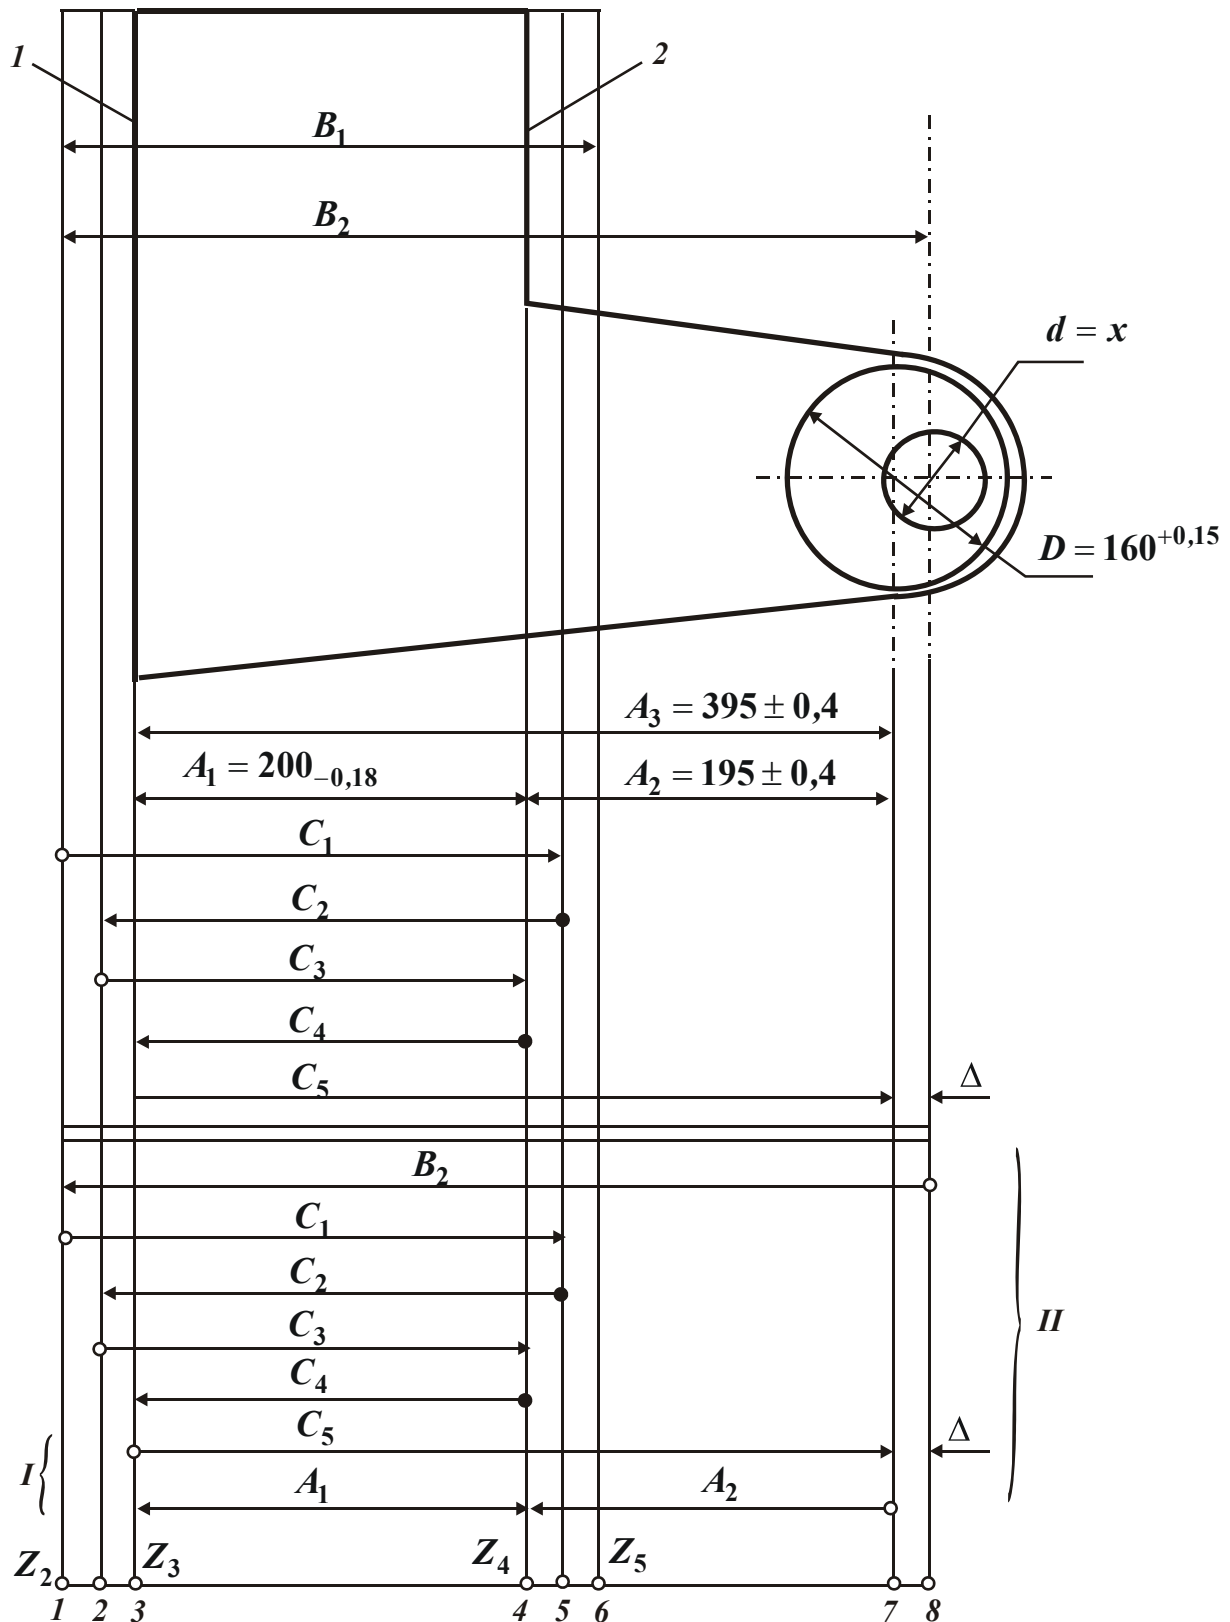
Размерная схема технологического процесса обработки корпусной детали.
